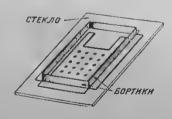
Коробка, служащая для изготовления второй половины формы.
